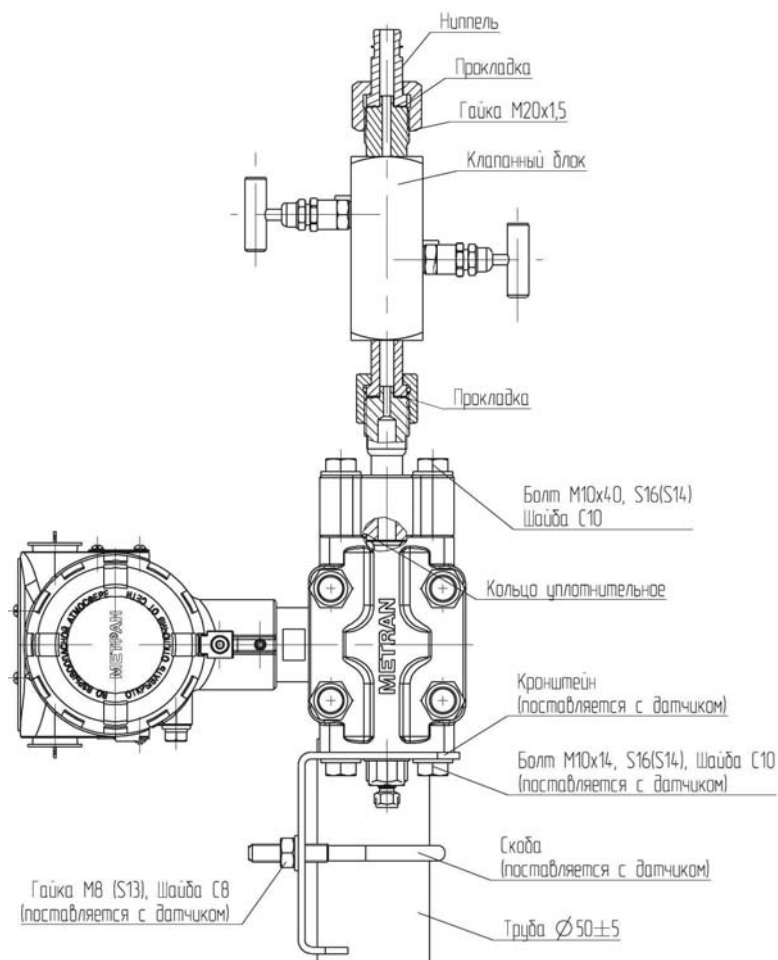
Вариант установки клапанного блока 0106 М Т для датчиков типа Метран-150CG. Габаритные и присоединительные размеры см.рис.21.
